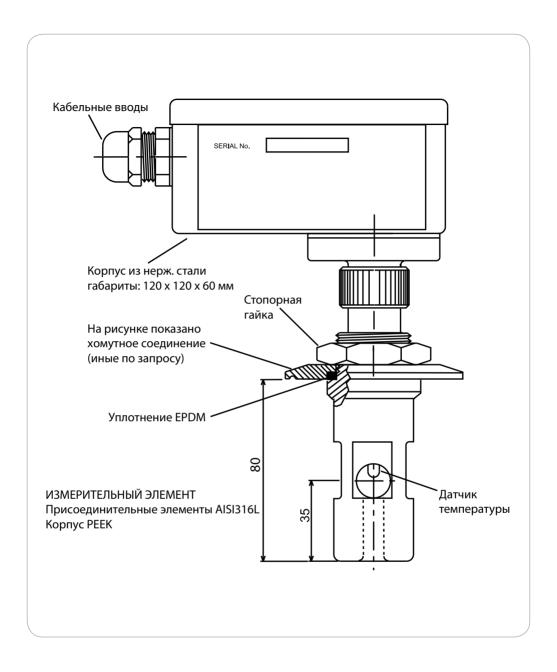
Габаритные размеры датчика IET40L с хомутным присоединением (вид сбоку)
